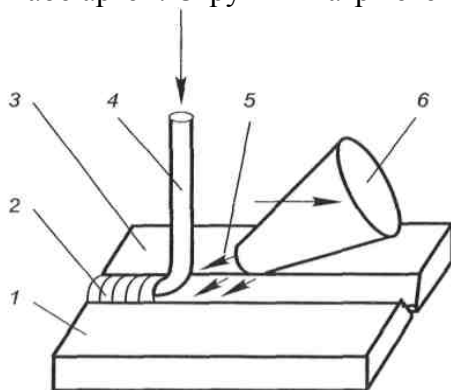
Схема зварювання нагрітим газом: 1,3 – зварювальний лист; 2 – зварний шов; 4 – присадний прутик; 5 – нагрітий газ; 6 – сопло
